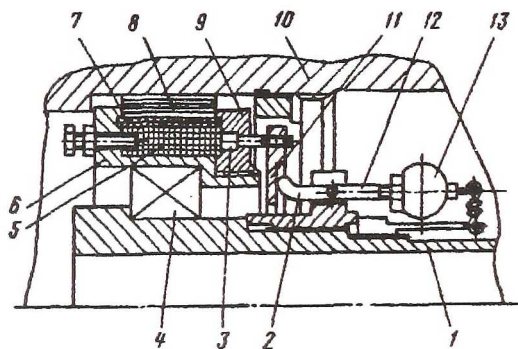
Упругодемпферная опора: 1 - ротор; 2, 12-плечи рычажного механизма; 3 - толкатель; 4 - подшипник; 5 - пластический материал; 6, 9 - элементы промежуточного звена; 7 - разрезная втулка; 8 - пакет гофрированных пластин; 10 - корпус; 11 - диск-нагнетатель; 13 - сосредоточенная масса
